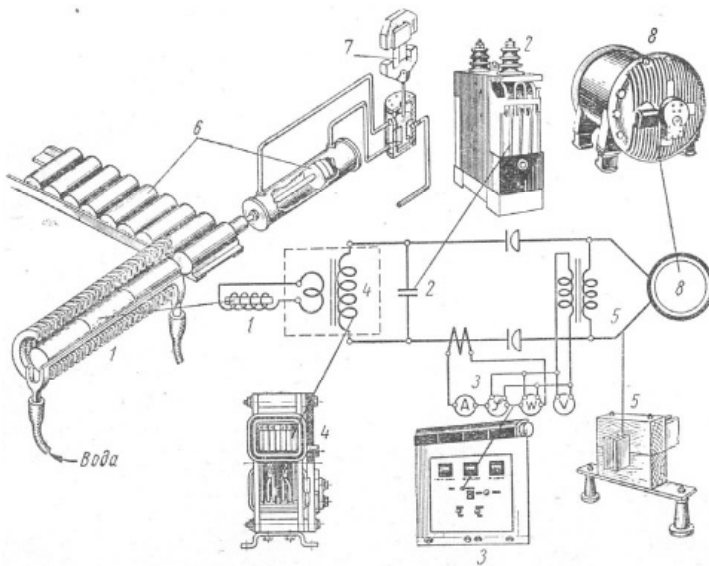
Схема индукционного нагревателя: 1 – индуктор с нагревательными заготовками; 2 – батарея конденсаторов; 3 – комплект измерительной аппаратуры; 4 – высокочастотный трансформатор; 5 – токопровод; 6 – механизм подачи заготовок; 7 – элемент автоматического управления механизмом подачи заготовок; 8 – высокочастотный генератор
